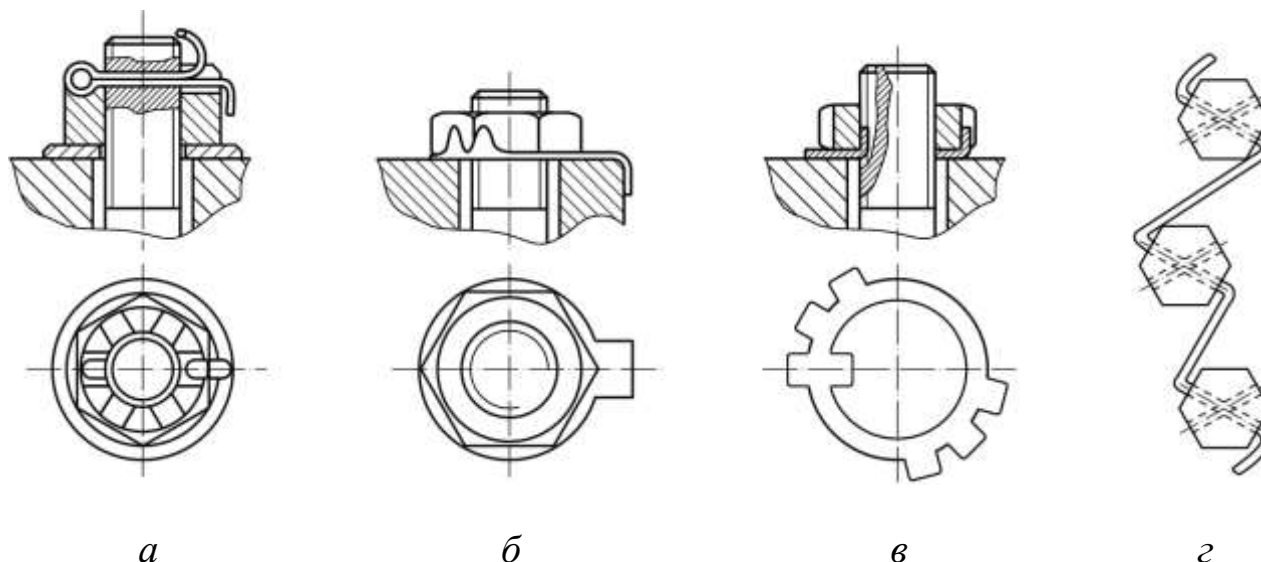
Способы стопорения резьбовых соединений специальными элементами
